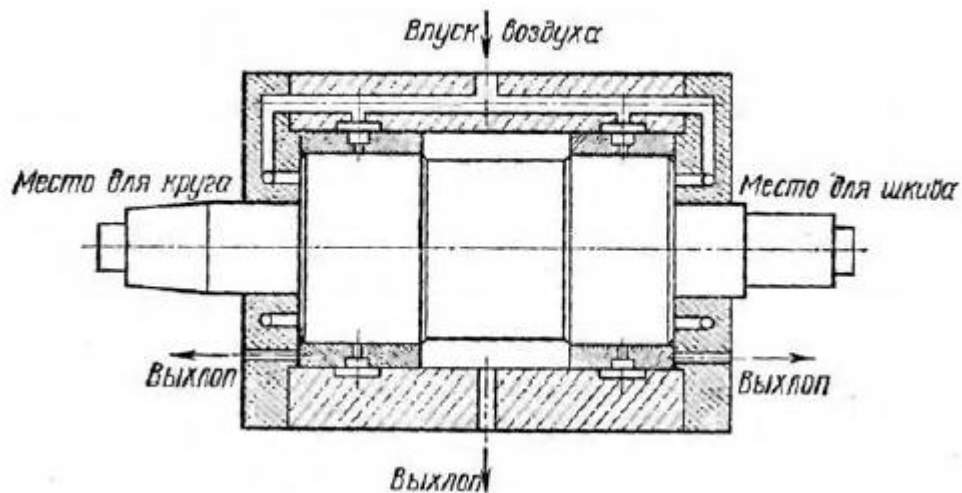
Вал с аэроэстатическими подшипниками
